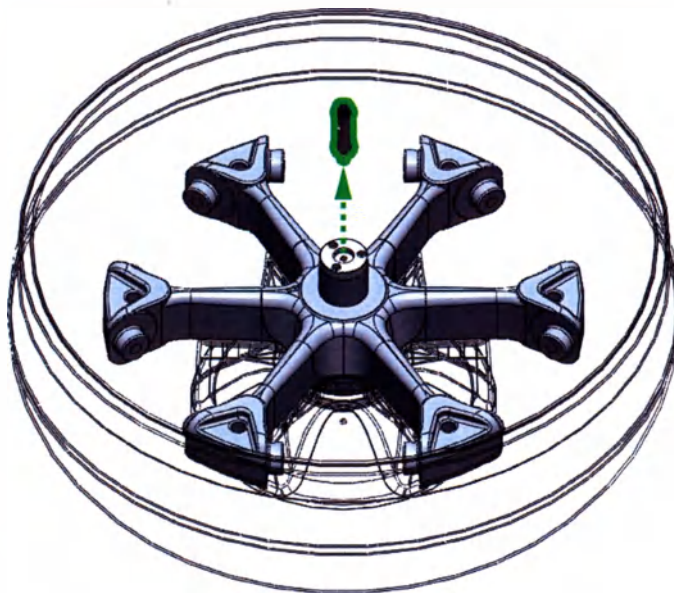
Извлечение крепежного винта ротора из приводного вала
